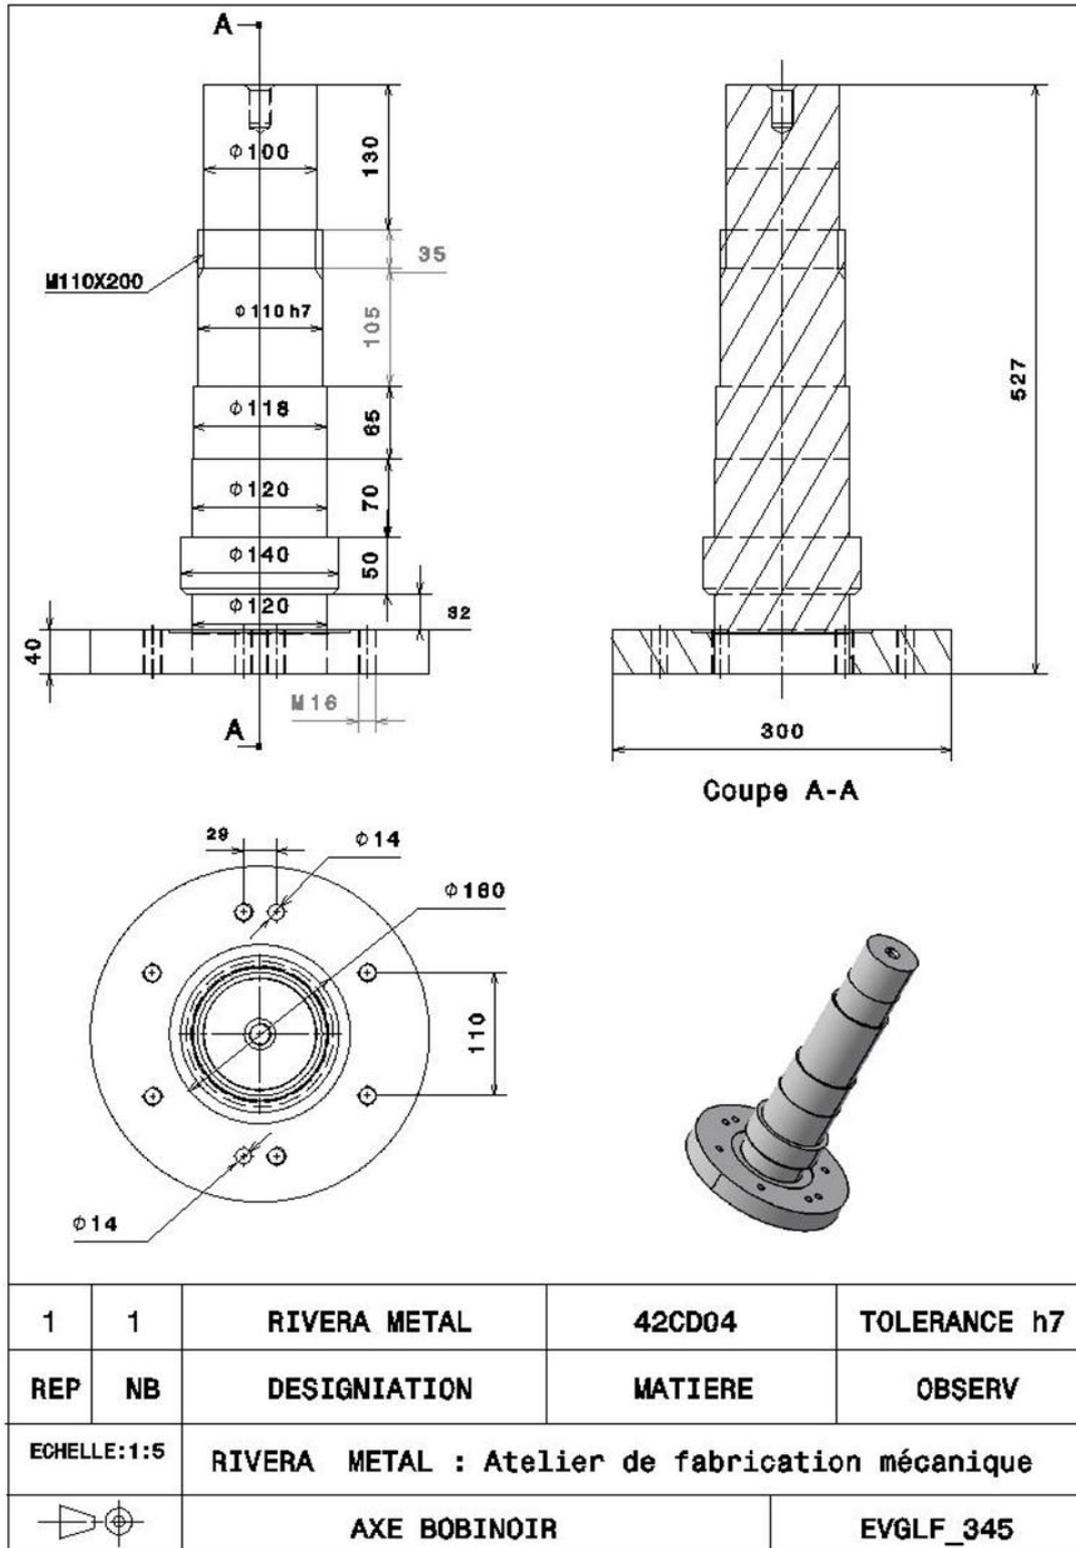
6 : Dessin de définition de l'arbre axe bobinoir
